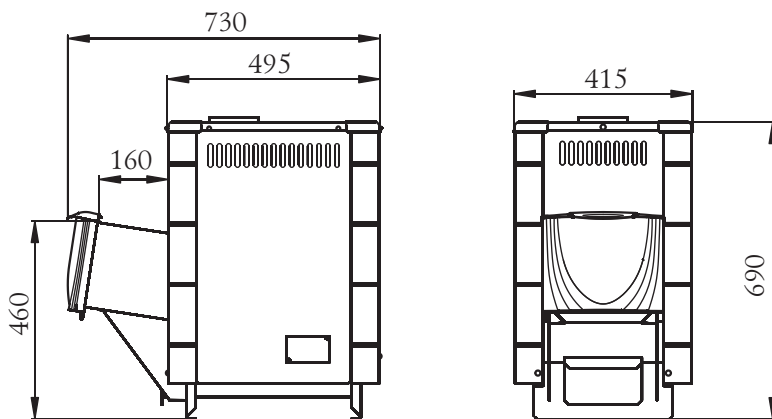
Габаритные размеры печи «Компакт» и «Компакт INOX».
